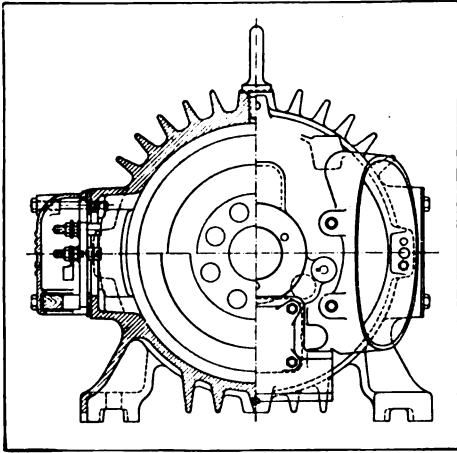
Motor mit Mantelkühlung (Querschnitt).
